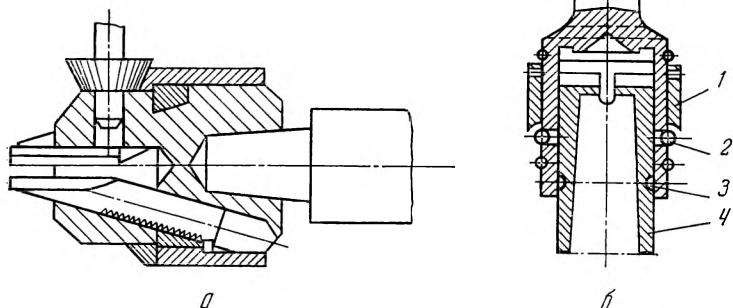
Приспособления для установки заготовок на столе сверлильного станка:
